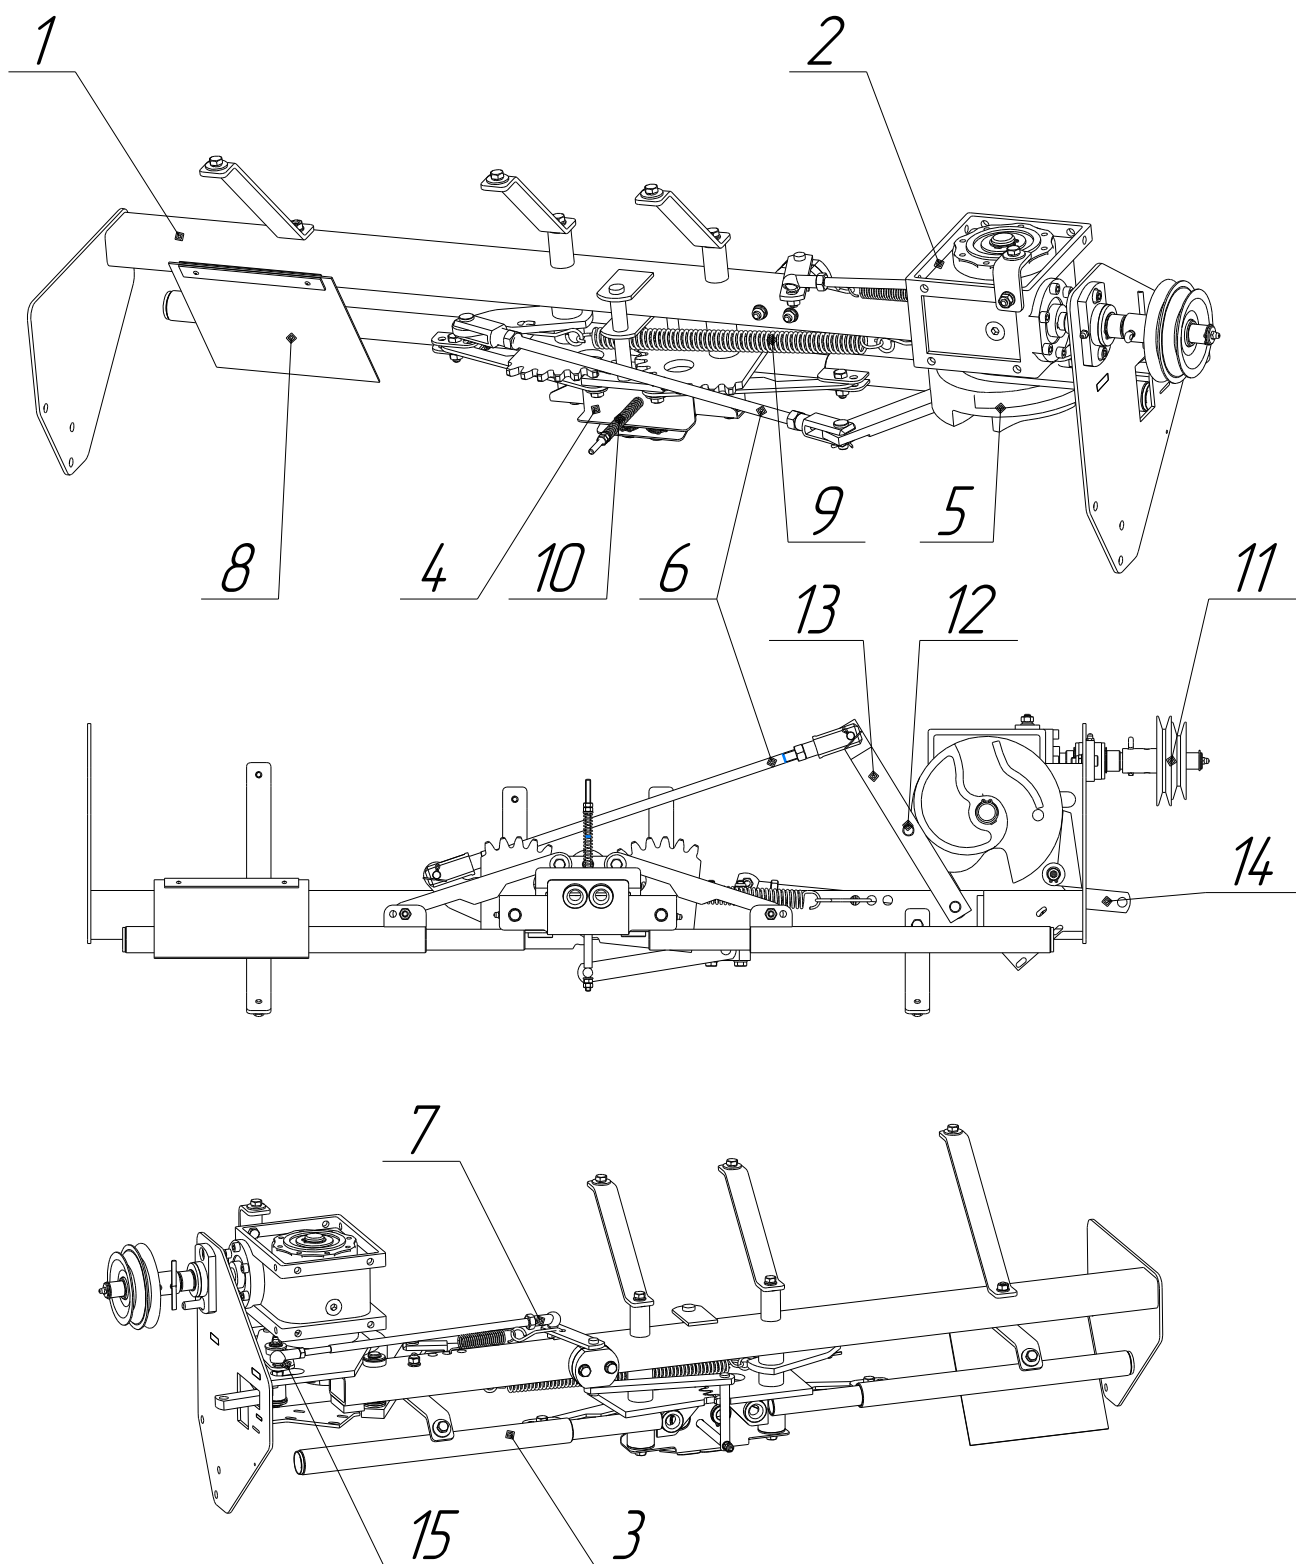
Механизм обвязки шпагатом: 1 – рама; 2 - редуктор червячный; 3 – направляющая шпагата; 4 – механизм тормоза шпагата; 5 – эксцентрик; 6 – тяга направляющих шпагата; 7 – привод тормоза шпагата; 8 – отбойник; 9 – пружина направляющих шпагата; 10 – пружина тормоза шпагата; 11 – шкив; 12 – ролик; 13 – рычаг привода направляющих шпагата; 14 – рычаг привода режущего устройства (спусковой механизм режущего устройства); 15 - рычаг привода тормоза шпагата.
